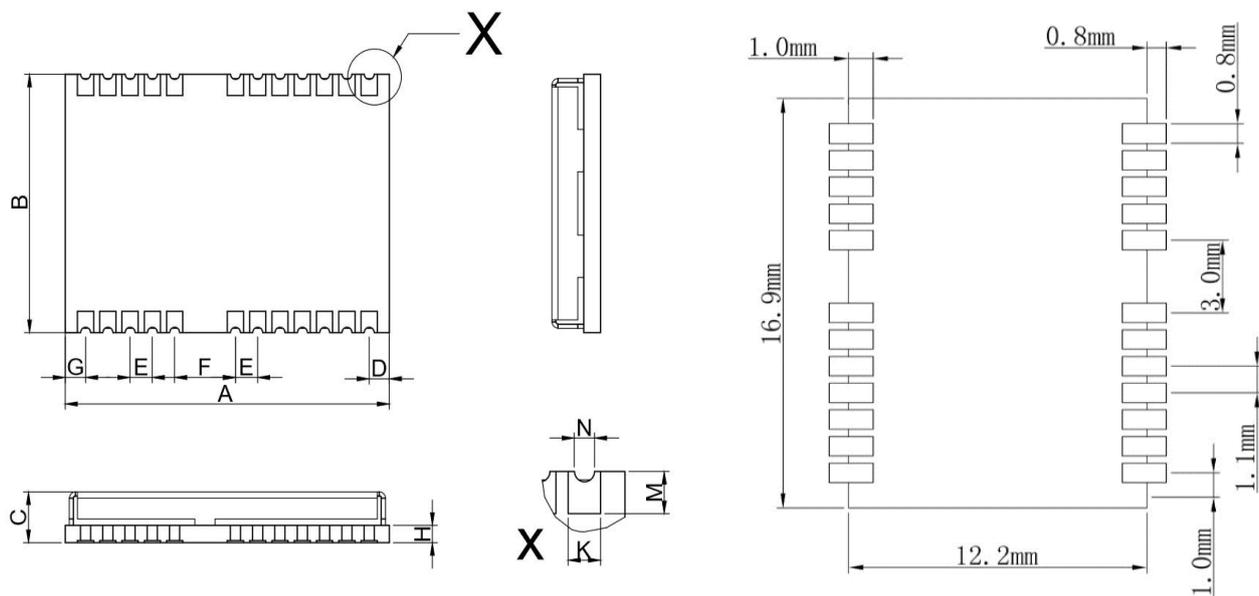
MXT909A 外形尺寸及 PCB 封装参考
